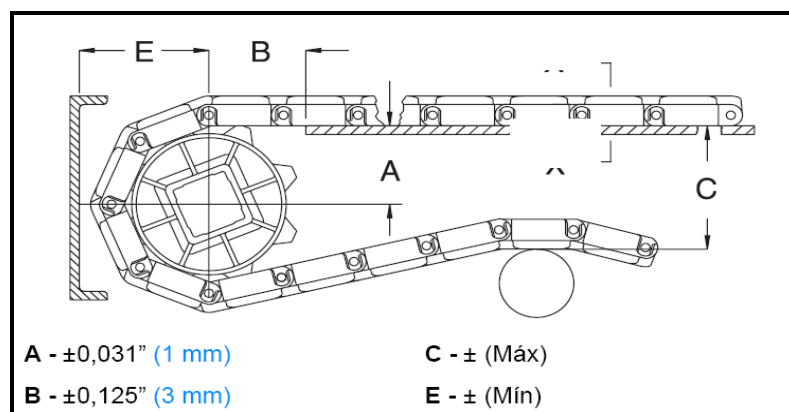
Detalle de dimensiones. Fuente: Intralox.
